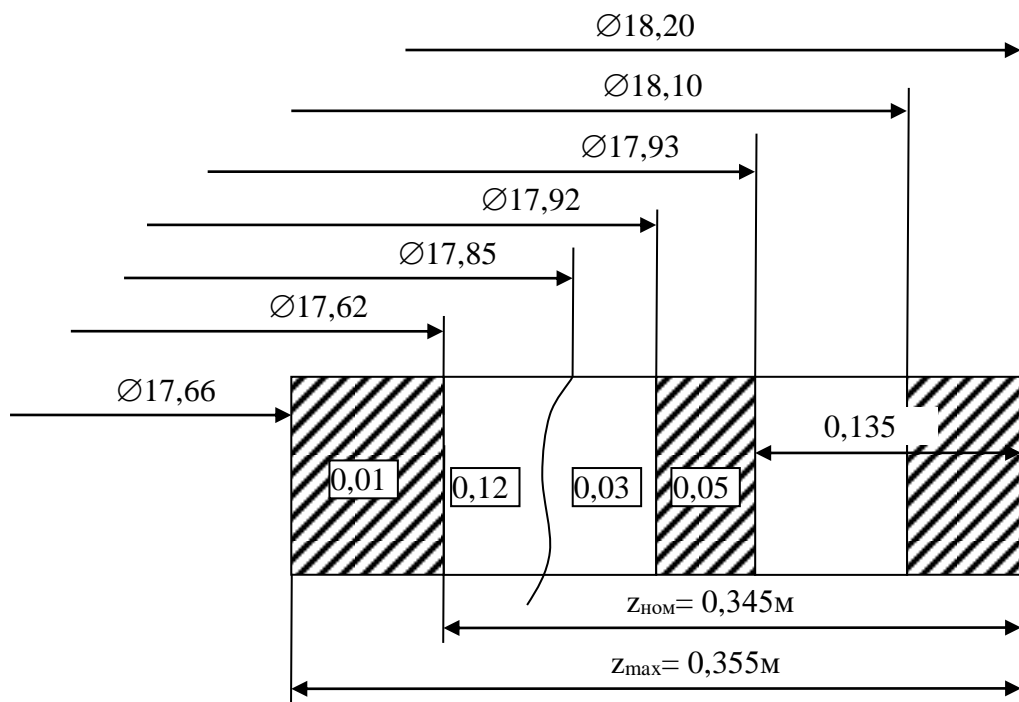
Схема визначення припусків і допусків при відновленні посадочних місць валу під підшипник ковзання
